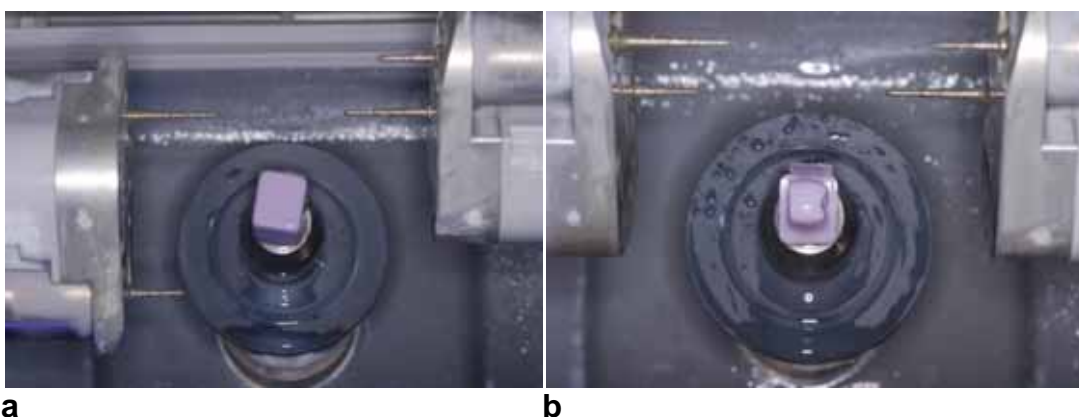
a) Bloco no início do processo de usinagem; b) Bloco no final do processo de usinagem.
